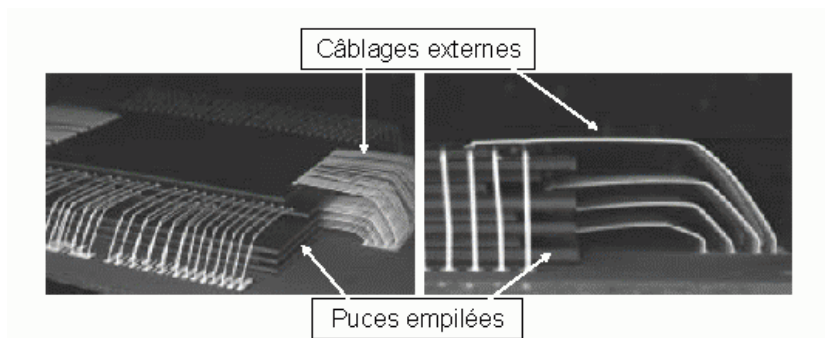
Packaging Multi-puces à 9 couches, Toshiba [Tos]
